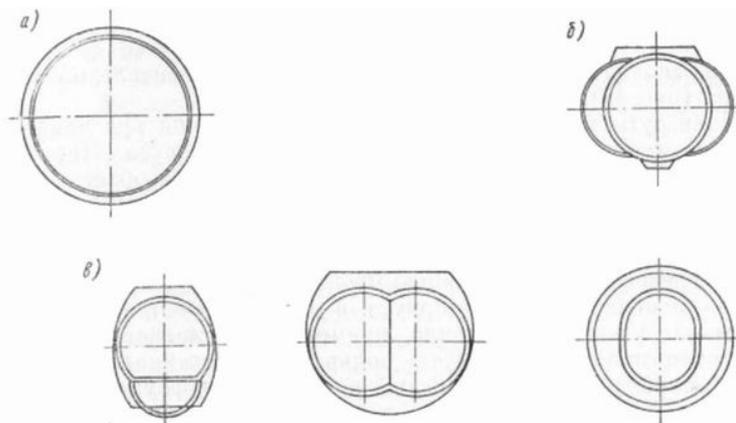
Конструкции поперечных сечений подводных лодок: а — однокорпусной; б — полуторакорпусной; в — двухкорпусной.
